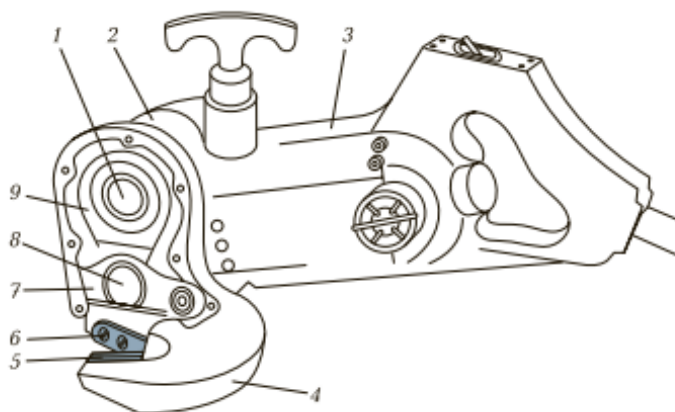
Ручные электровибрационные ножницы: 1 — эксцентриковый вал; 2 — корпус ножовочной головки; 3 — корпус; 4 — скоба; 5 — нижний нож; 6 — верхний нож; 7 — рычаг; 8 — палец; 9 — шатун
